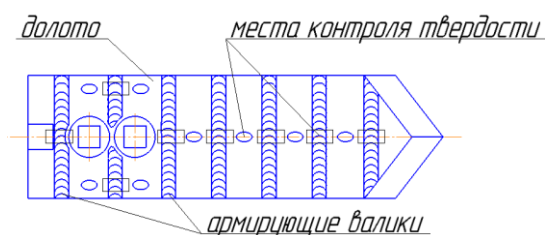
Схема наплавки на рабочей поверхности перпендикулярно боковым сторонам и места контроля твердости
